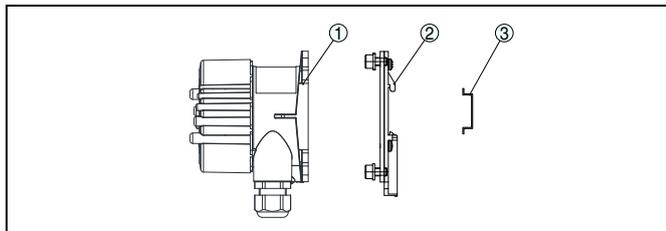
VEGADIS 81 и 82 с корпусом из алюминия или нержавеющей стали, для монтажа на несущей рейке
